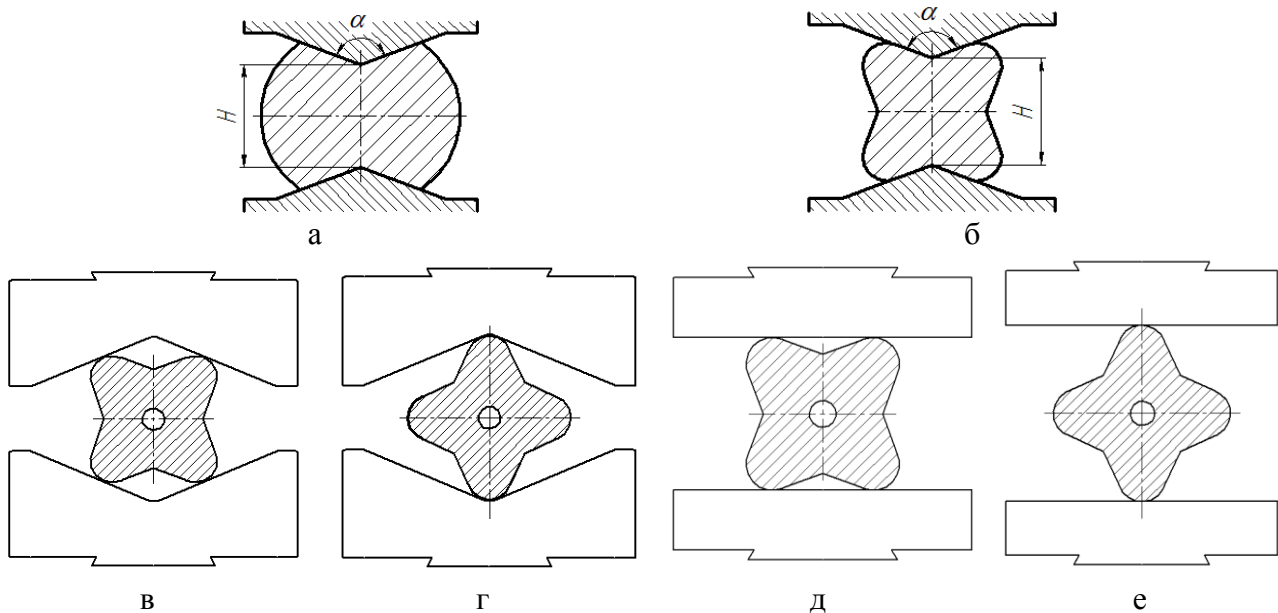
Переходыковки выпуклыми клиновыми бойками:
